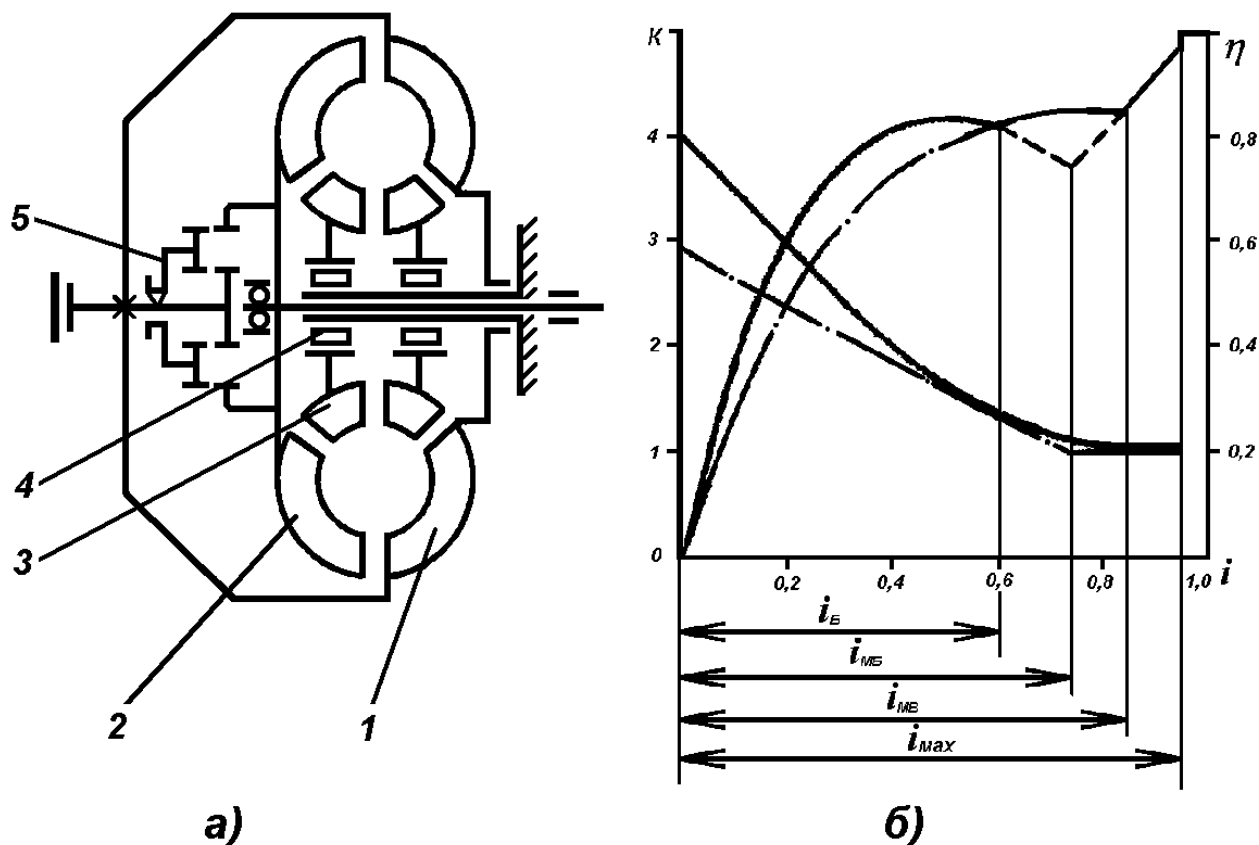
Одноступенчатый гидротрансформатор с двумя реакторами и зубчатой муфтой блокировки:
